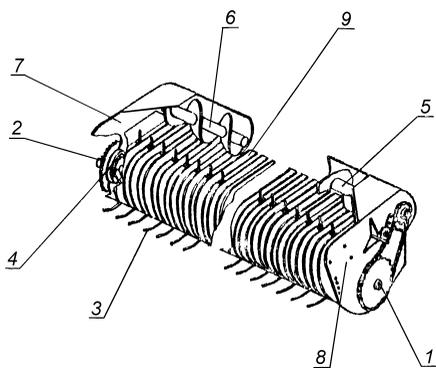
Подборщик: 1 – приводной вал; 2 – предохранительная муфта; 3 – пружинные зубья; 4 – направляющая дорожка; 5 – левый шнек; 6 – правый шнек; 7 и 8 – боковины; 9 – скат
